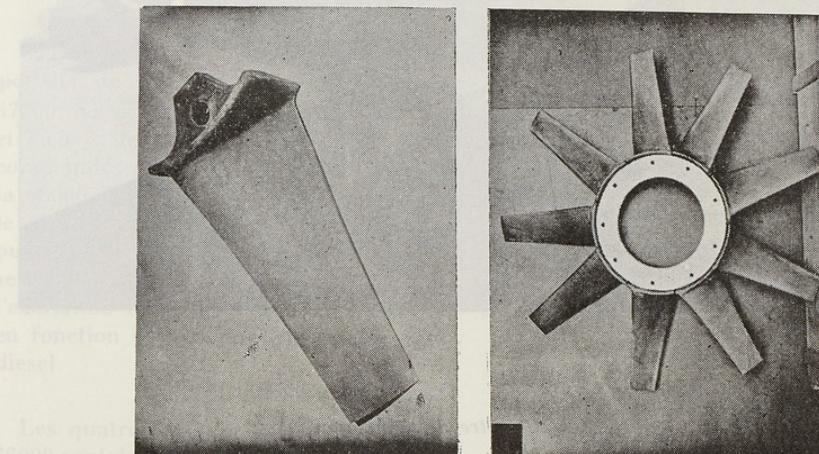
Pale et rotor de ventilateur des radiateurs.
